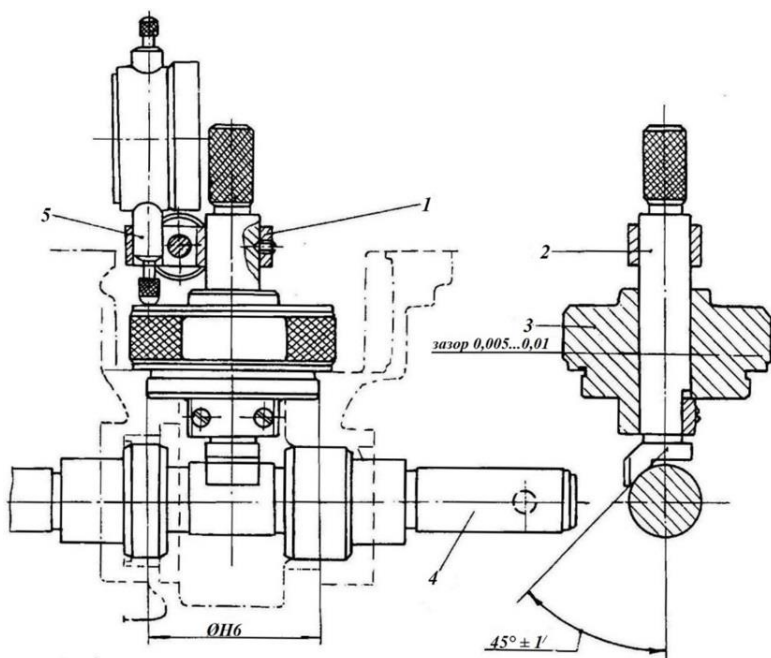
Приспособление для контроля пересечения двух осей отверстий картера
